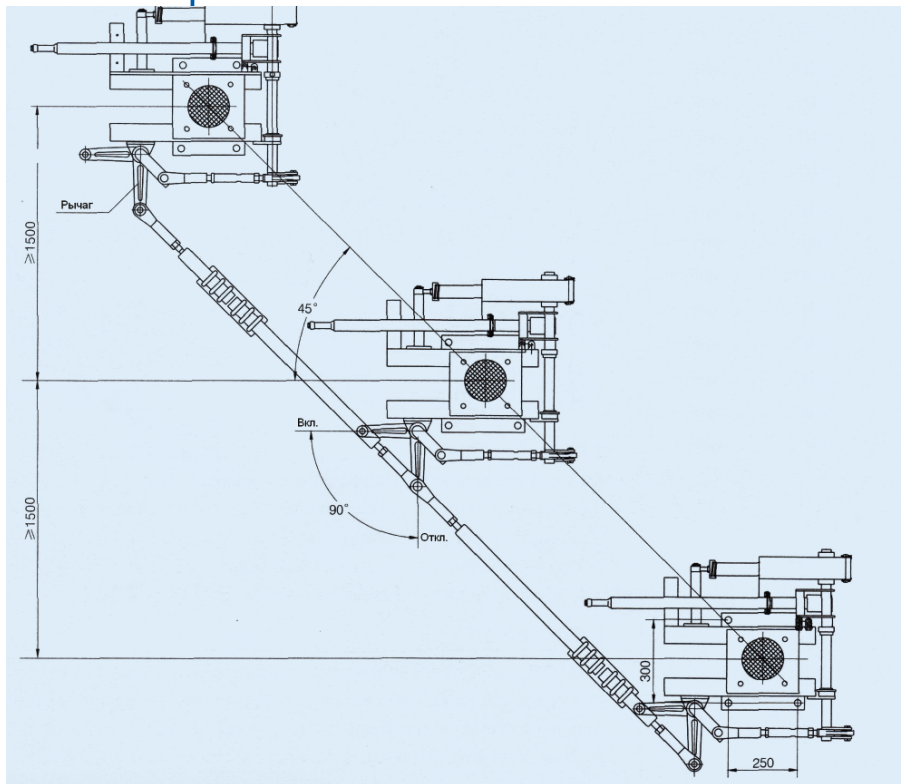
Внешний вид и размеры заземлителя JW□-126
